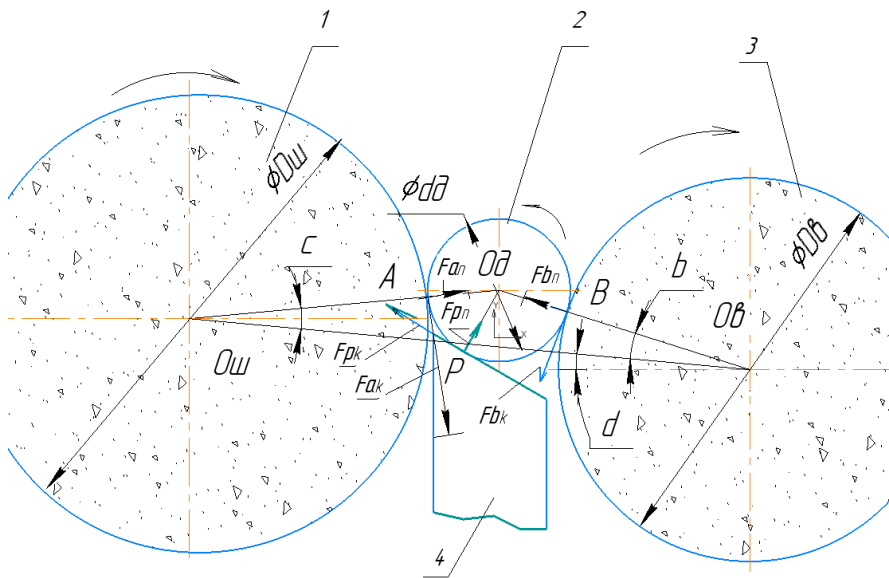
Схема сил при проходном бесцентровом шлифовании (центры осей кругов расположены не на горизонтальной прямой): 1 – шлифовальный круг; 2 – обрабатываемая деталь; 3 – ведущий круг; 4 – опорный нож
